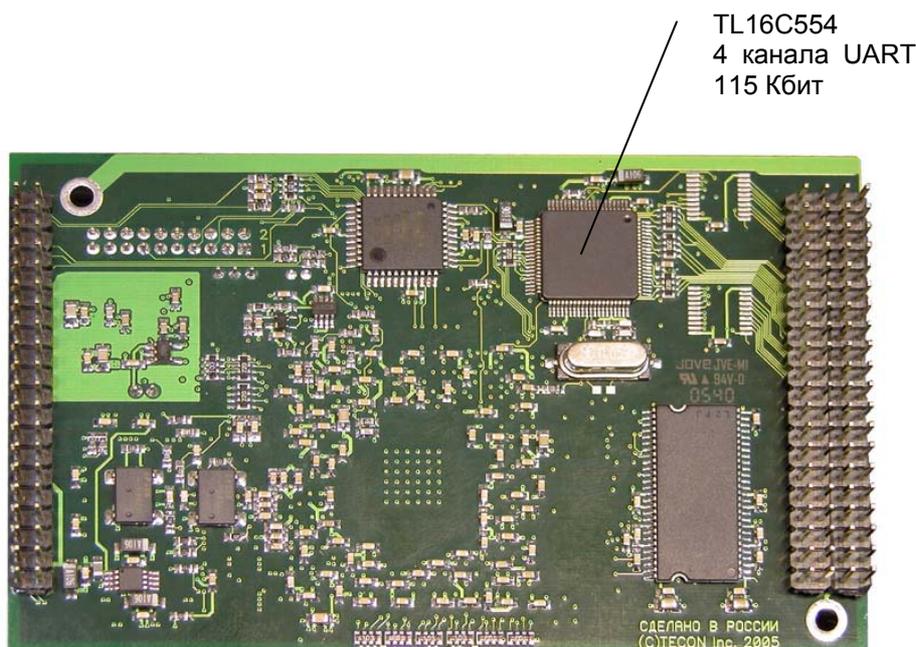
Внешний вид процессорного модуля t-mezon (вид снизу)
